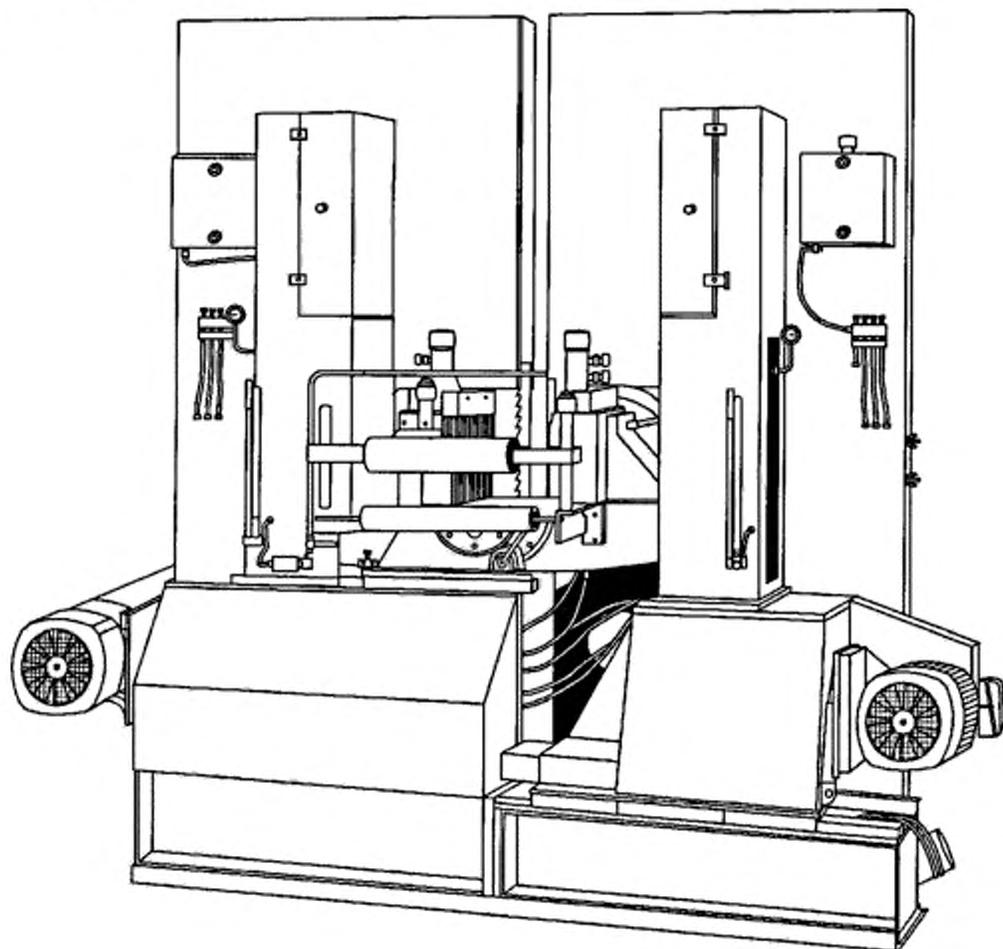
Пример сдвоенного ленточнопильного делительного станка с противоположным расположением агрегатов ленточной пилы
